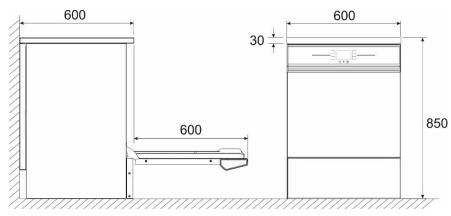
Disegno schematico, dimensioni ingombro del prodotto
